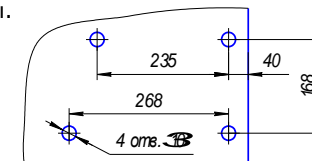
Схема расположения отверстий в столе для крепления машины
